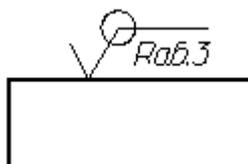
Обозначение одинаковой шероховатости поверхностей образующих замкнутый контур
